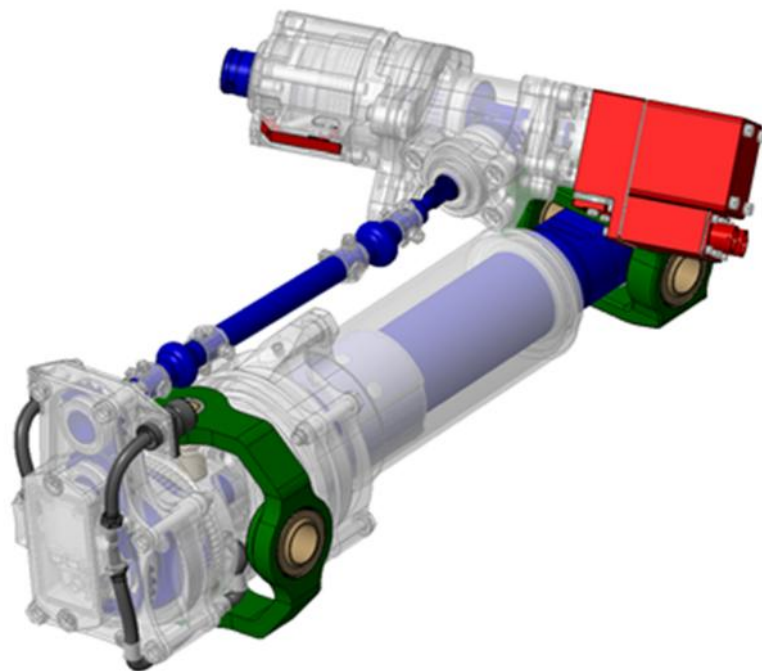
WOT Aktuator design mit Down Drive Shaft und Down Drive Gearbox
